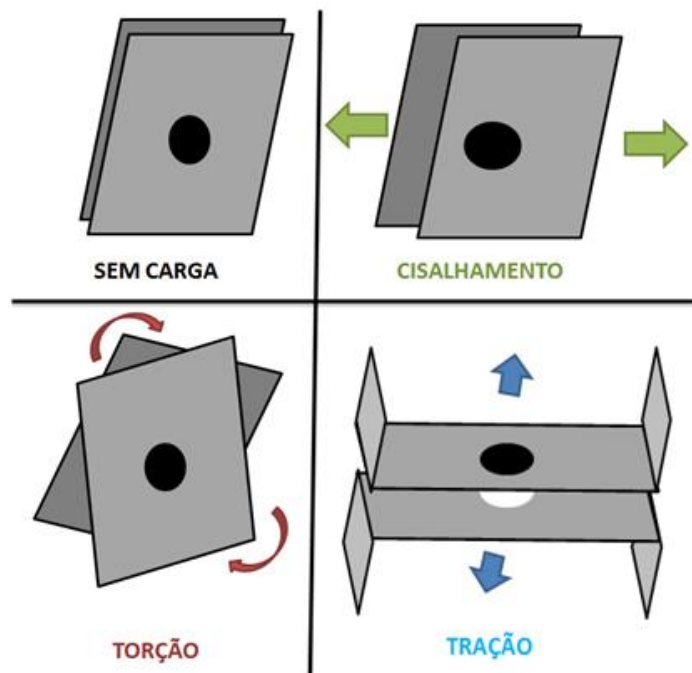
Principais Esforços em um Ponto de Solda
